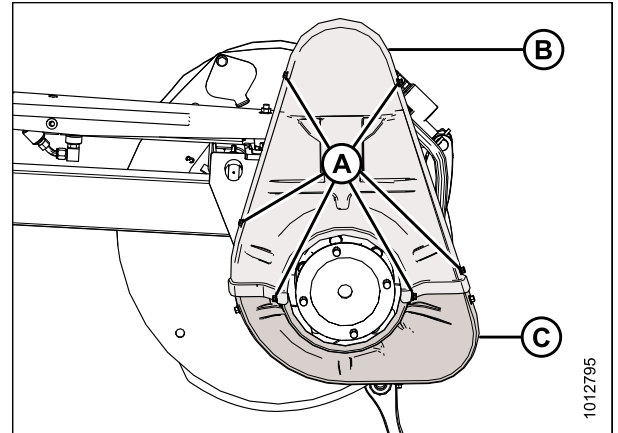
Крышка привода — сдвоенное мотовило
